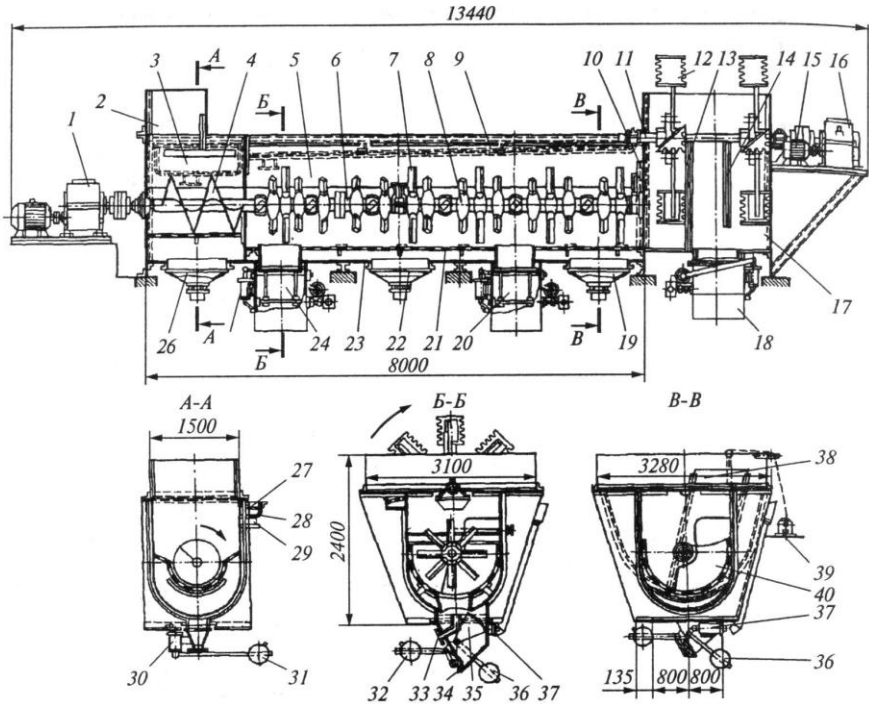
Бурякомийка КМЗ-57М: 1 – редуктор; 2 – лоток; 3 – приймальна частина; 4 – шнек; 5 – миюча частина; 6 – вал; 7 – кулачки; 8 – муфти; 9 – жолоб; 10; 13; 14 – перегородки; 11 – вал; 12 – ковші; 15 – електродвигун; 16 – редуктор; 17 – викидаюча частина; 18; 20; 24 – каменевловлювачі; 19; 22; 26 – пісковловлювачі; 21 – перфороване днище; 23 – суцільне днище; 25; 30; 37 – гідроциліндри; 27 – перфороване днище; 28 – суцільне днище; 29 – штуцер відводу води; 31; 32; 36 – противаги; 33 – труба для води; 34 – кришка; 35; 38 – шибері; 39 – лебідка; 40 – отвір
